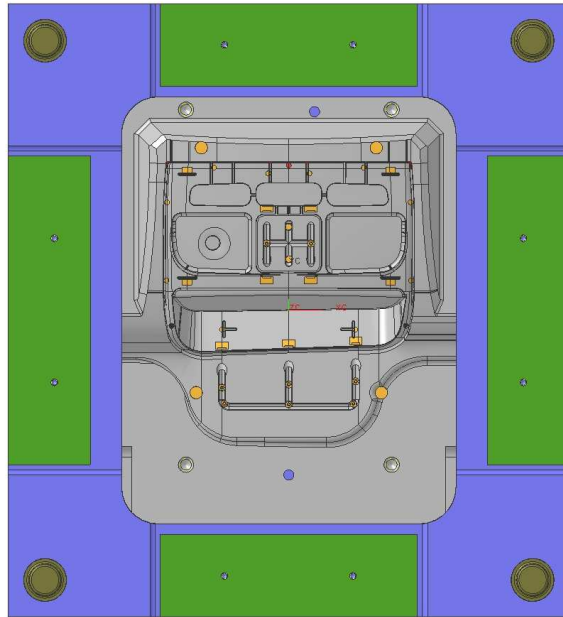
Lage des Formeinsatzes im Werkzeugmittelpunkt
